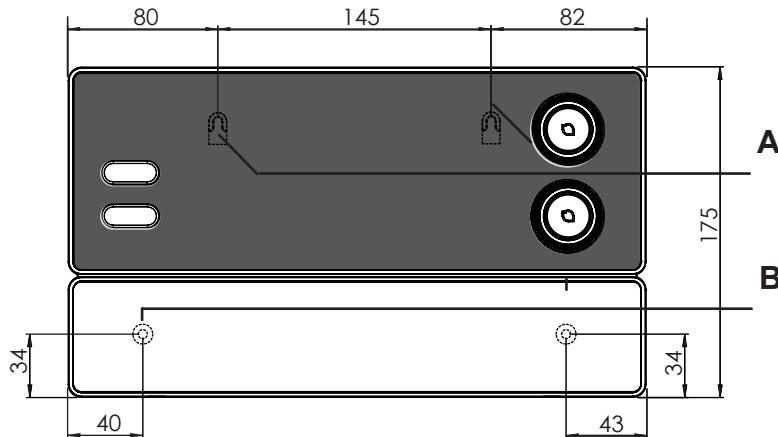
Posizione del dispositivo di sospensione e dei fori di montaggio (misure in mm)
